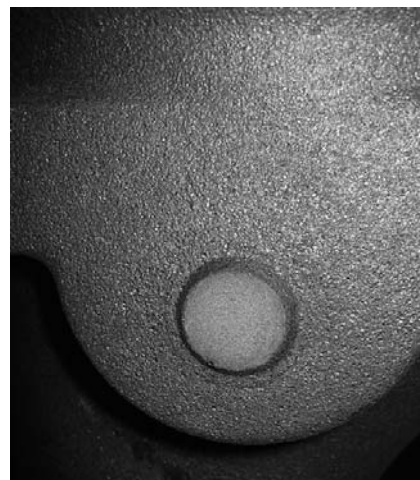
Bruchstelle nach dem Abschlagen des Speiserrestes
